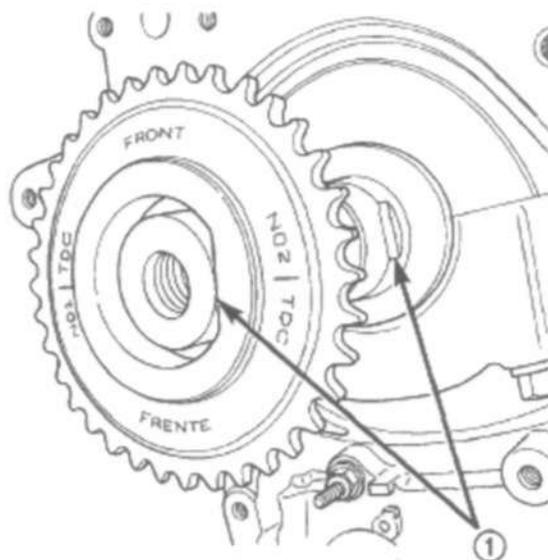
Центрирование звездочки балансировочного вала относительно коленчатого вала
